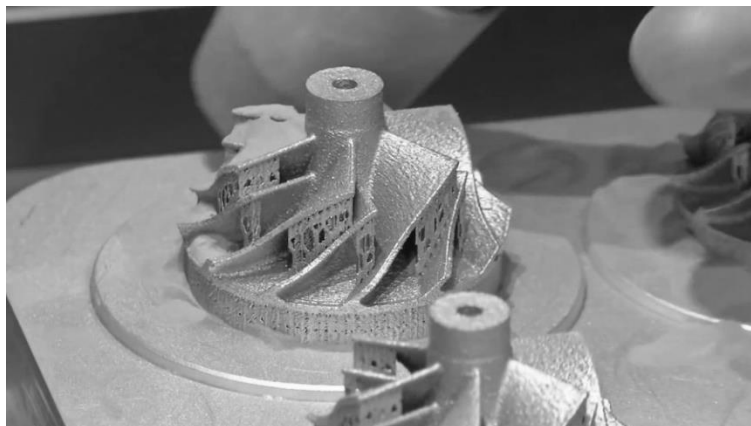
Рабочее колесо компрессора, напечатанное на 3D принтере
